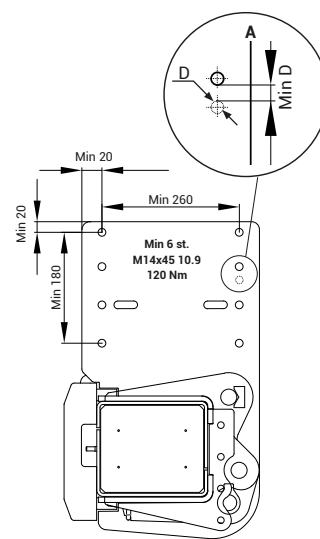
Die Rahmenhalterung mit mindestens 6 Schrauben befestigen (M14x45 10.9). A = Neues Loch
